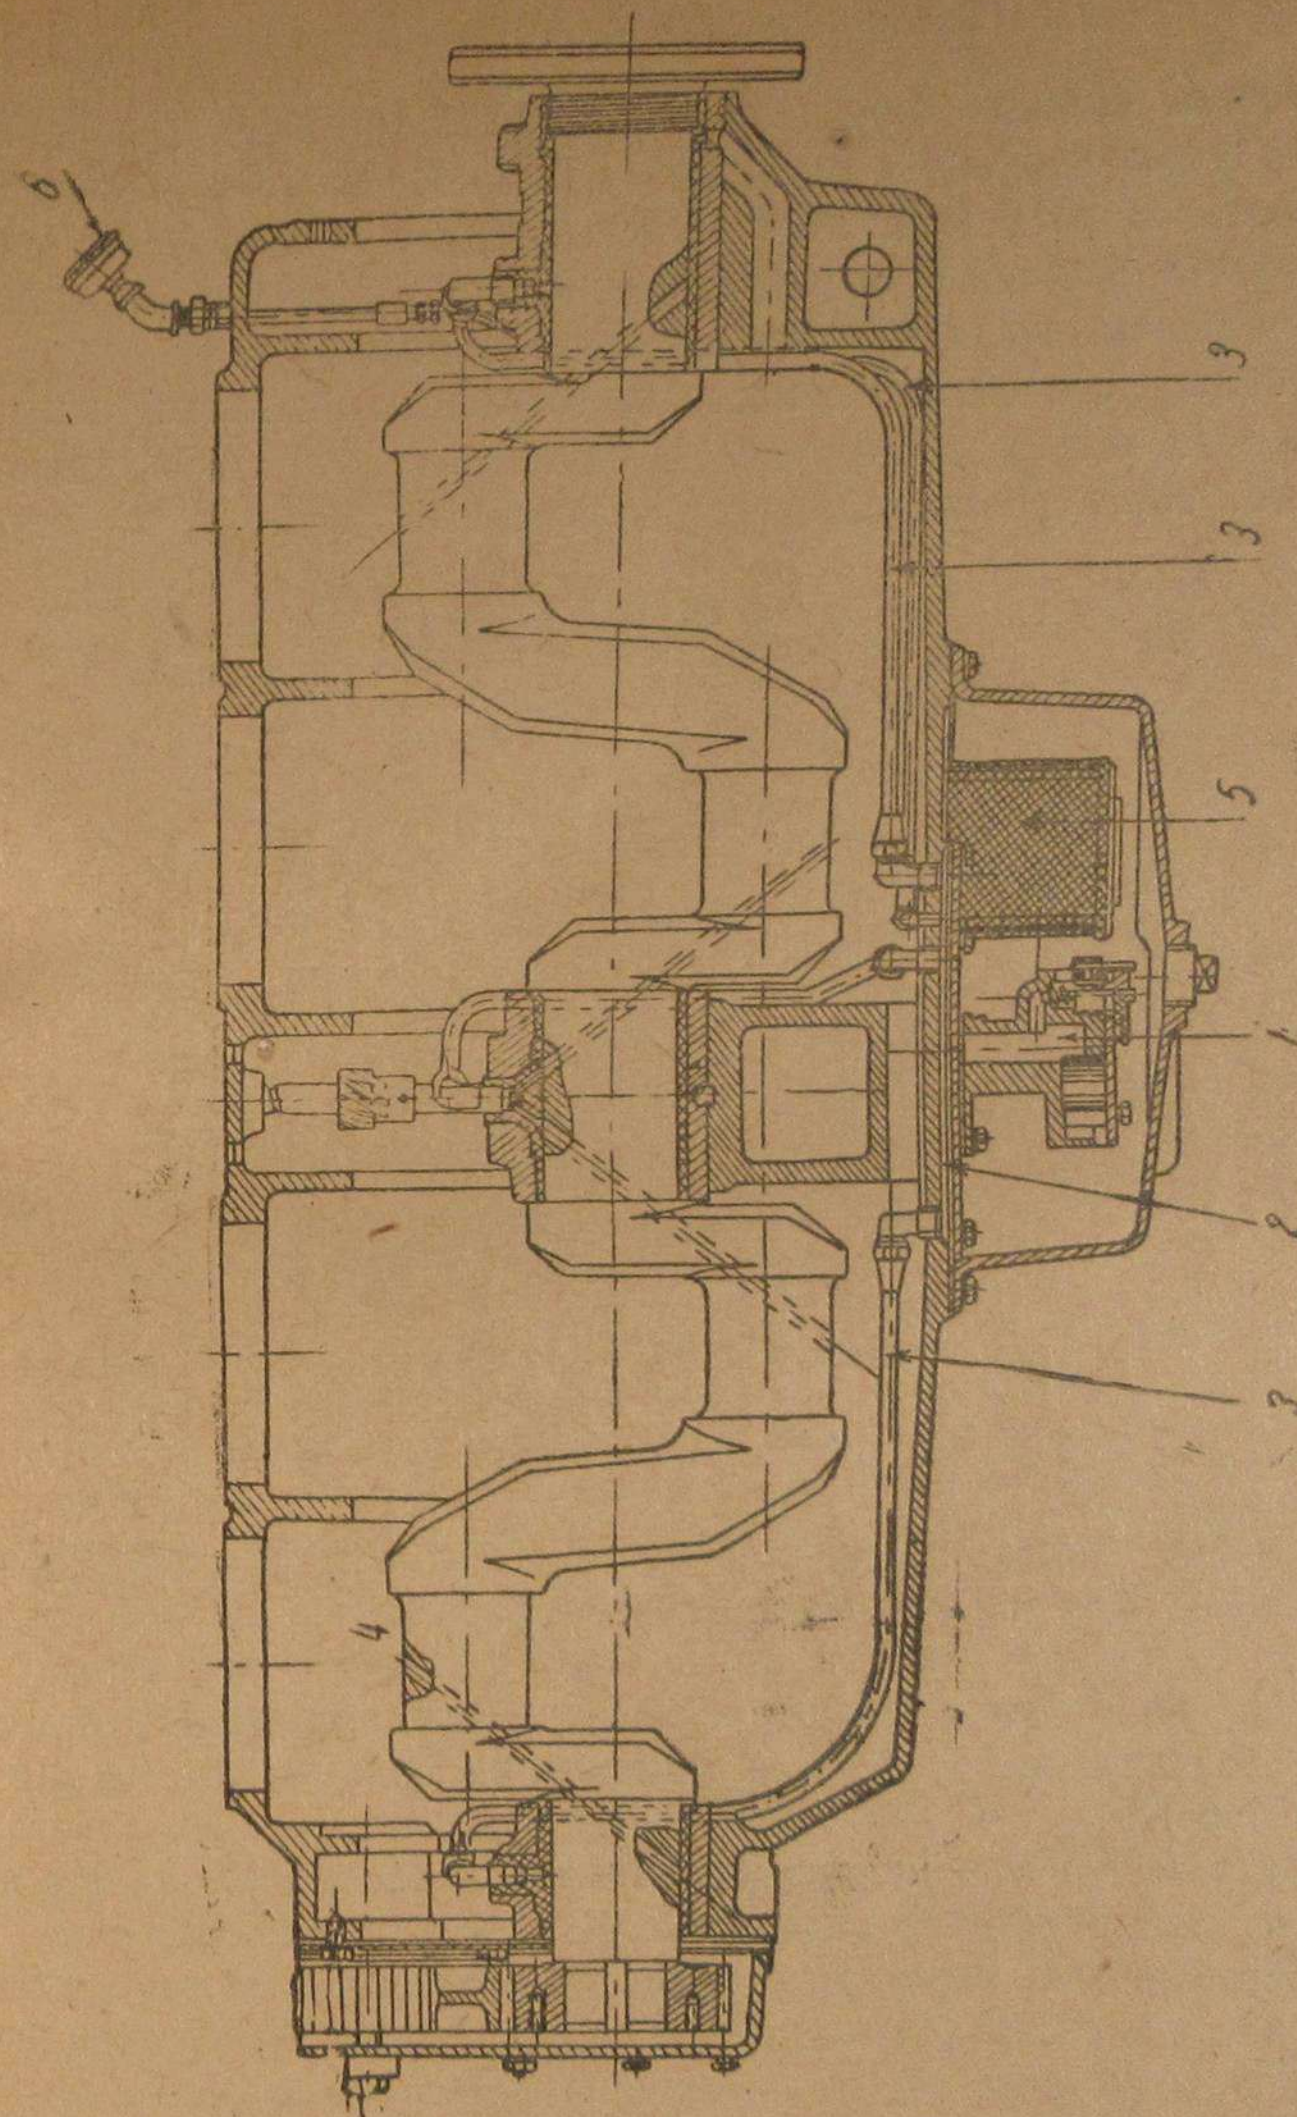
Схема смазки двигателя ЧТЗ «Сталинец-60»
